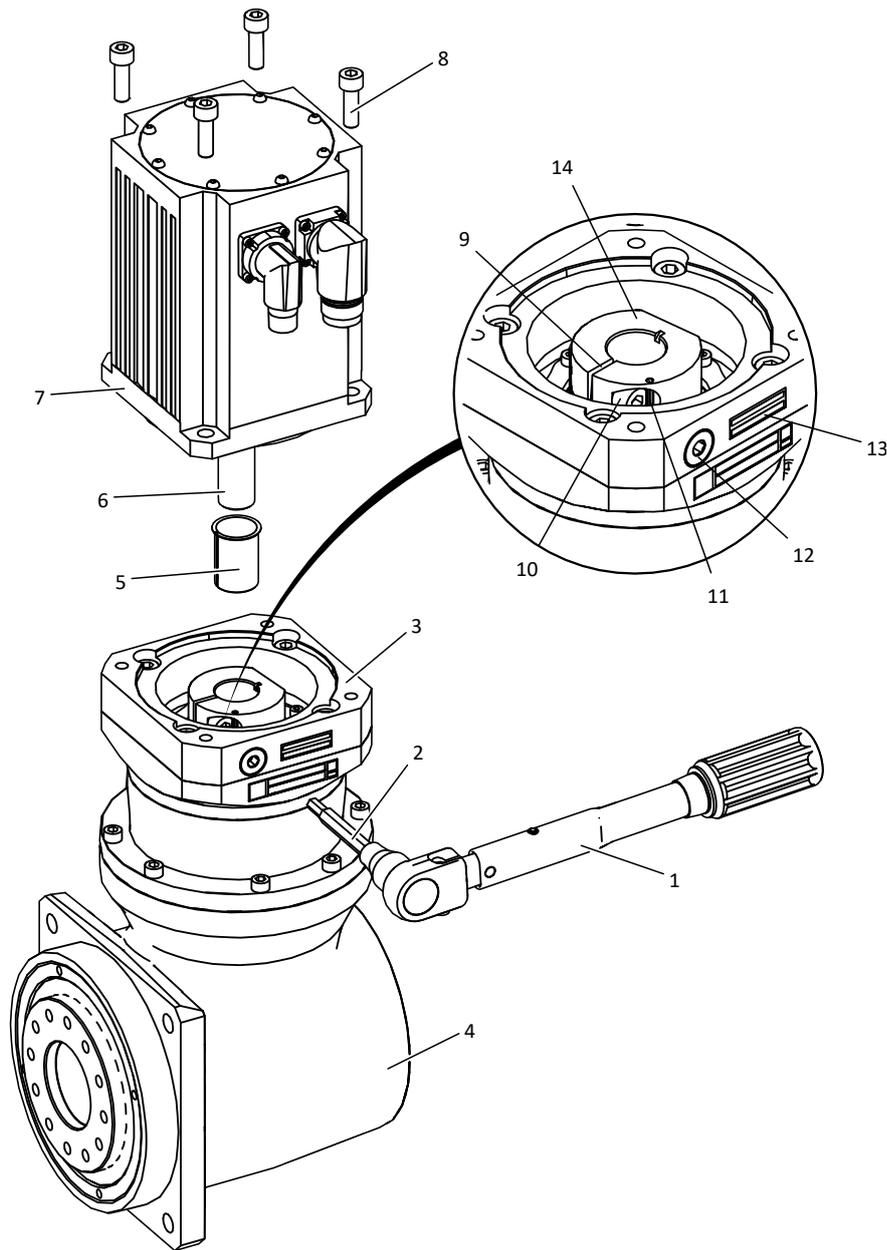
Montage eines Motors an ein Servowinkelgetriebe KS mit Flanschwellen und Motoradapter
